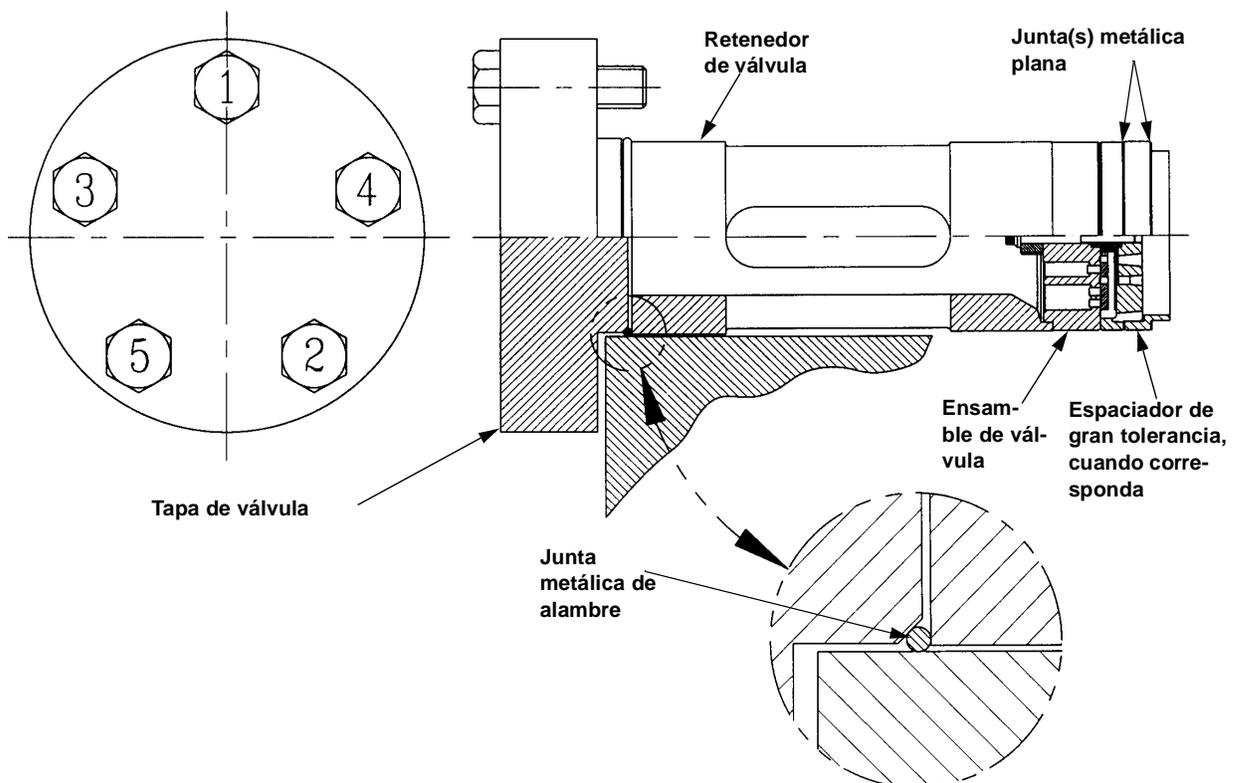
ENSAMBLE DE TAPA DE VÁLVULA DE ALTA PRESION
